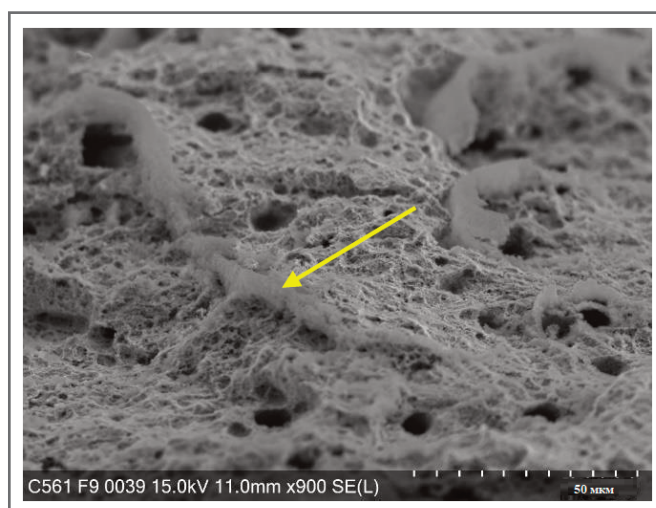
Ориентированные чашечные изломы на поверхности разрушения образца F9, указывающие на механизм сдвига
